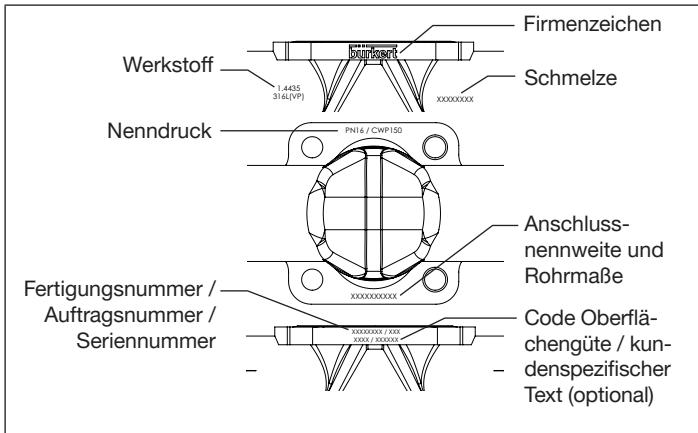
Beschriftung der Rohrumbformgehäuse (VP)
